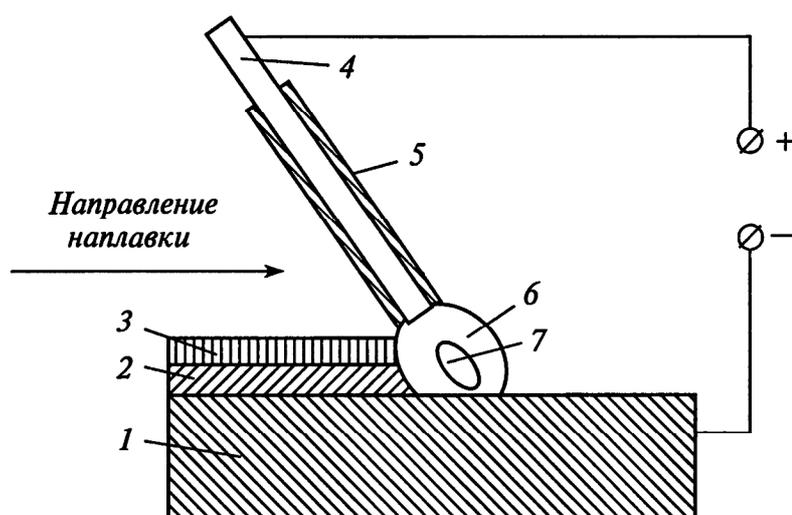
Схема ручной наплавки: 1 – основной металл;
